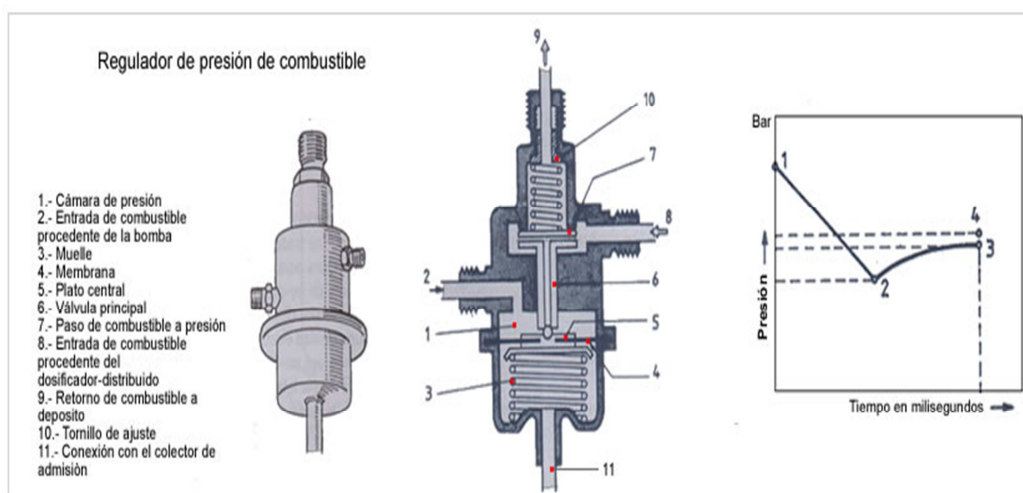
Regulador de Presión de Combustible (Sistema KE-Jetronic)
